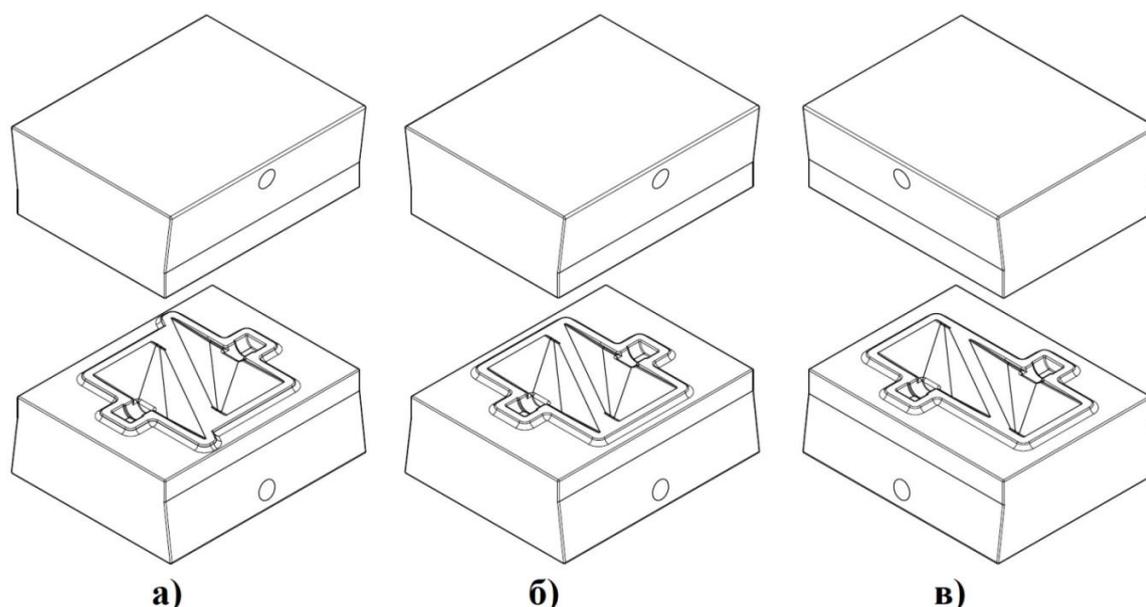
3D модели штамповых вставок для штамповки сдвоенных поковок из алюминия: а – оси хвостовиков поковок совпадают с осью заготовки располагаемой в штампе; б – оси хвостовиков поковок смещены друг относительно друга, крайние точки боковых поверхностей лежат на одной линии; в – оси хвостовиков поковок смещены друг относительно друга, верхняя часть первой поковки лежит на одной линии с нижней частью второй поковки
